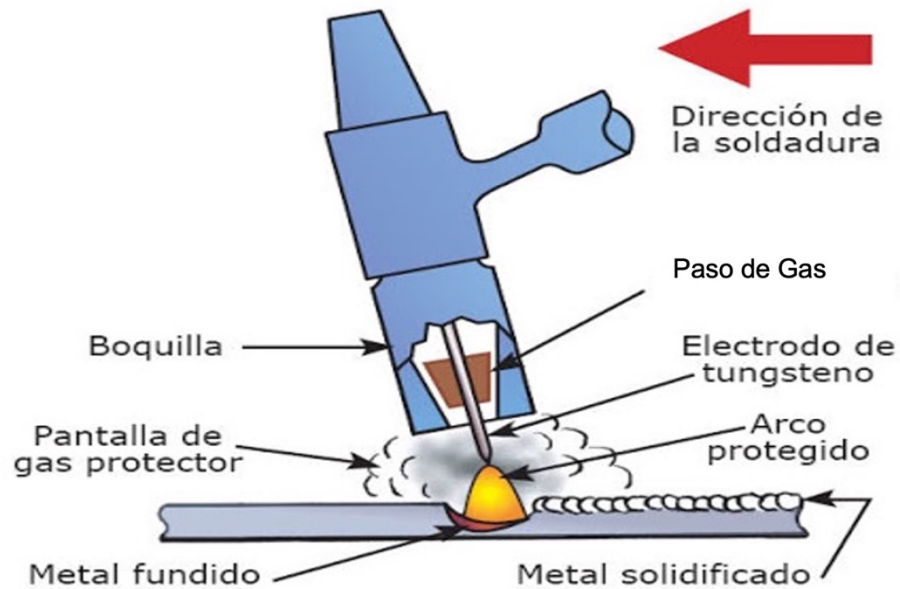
Representación esquemática del proceso de soldadura GTAW que muestra la antorcha, boquilla, protector de gas, electrodo de W y el metal base donde se aplica la soldadura [18]
